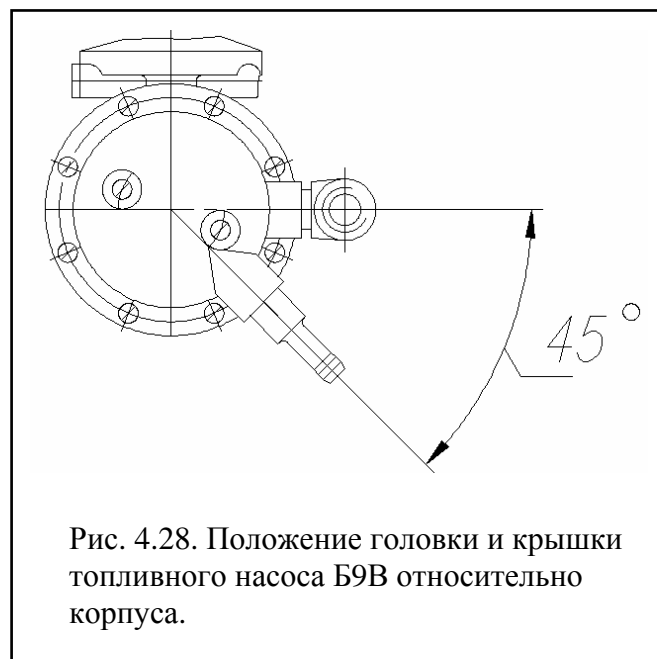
Положение головки и крышки топливного насоса Б9В относительно корпуса.
